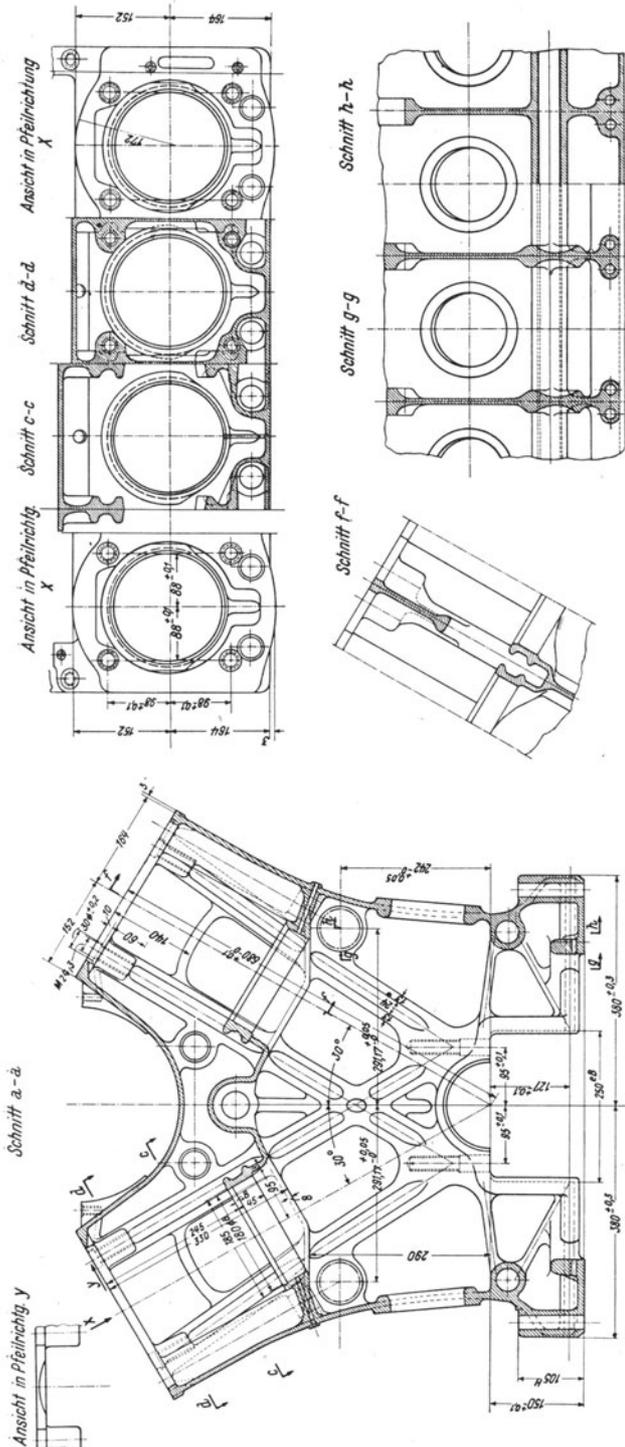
Kurbelgehäuseoberteil aus Silumin für den V-Motor.
